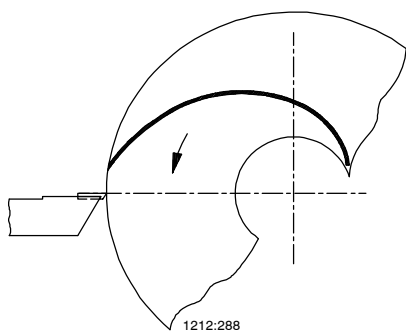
Направление вращения при обтачивании сварного колеса из хромникелевой стали
